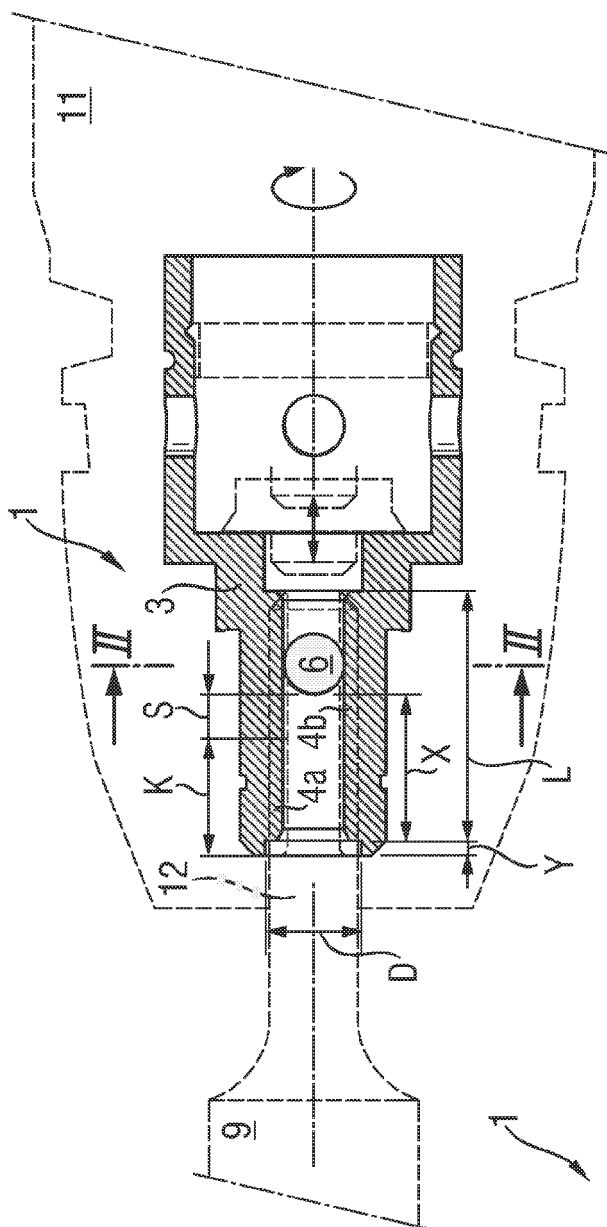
als Werkzeugaufnahme im Längsschnitt
